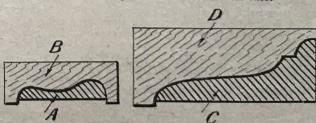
Placage des moulures: A, moulure à plaquer; B, calle (cadres); C, corniche de meuble à plaquer; D, calle.
